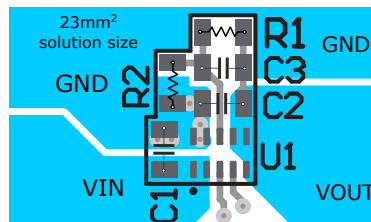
用于可调节器件的 TPSM82A823x PCB 布局（根据元件列表的 BOM，C2 为 2 × 22μF）
